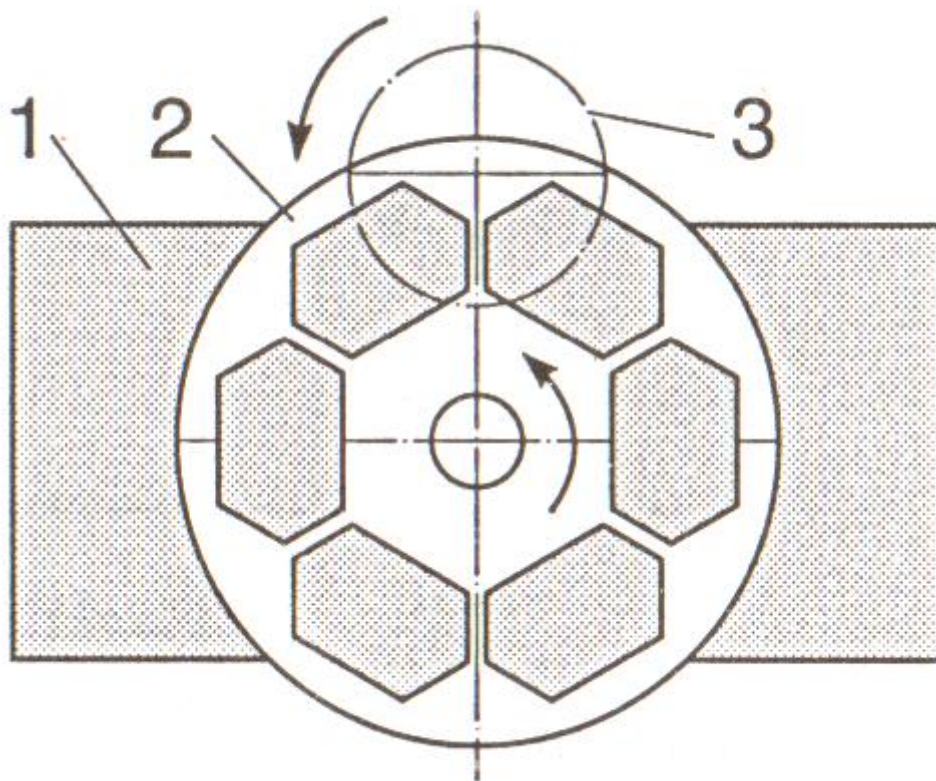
Групова обробка корпусних деталей на вертикально – фрезерному верстаті: 1 – станина верстата; 2 – стіл; 3 – торцева фреза
